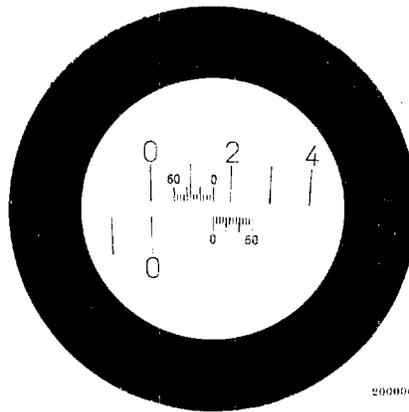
Scheinbares Sehfeld des Optischen Universal-Winkelmessers
